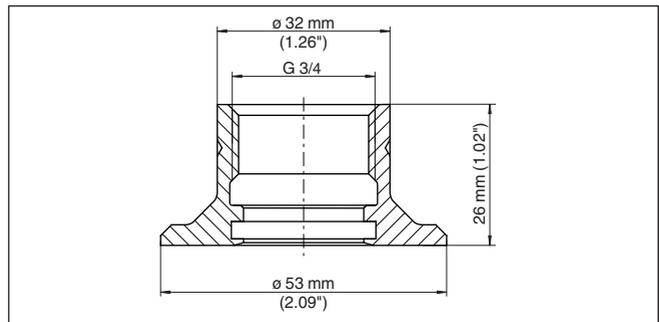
Medidas racor para soldar G $\frac{3}{4}$ (DIN 3852-X)
